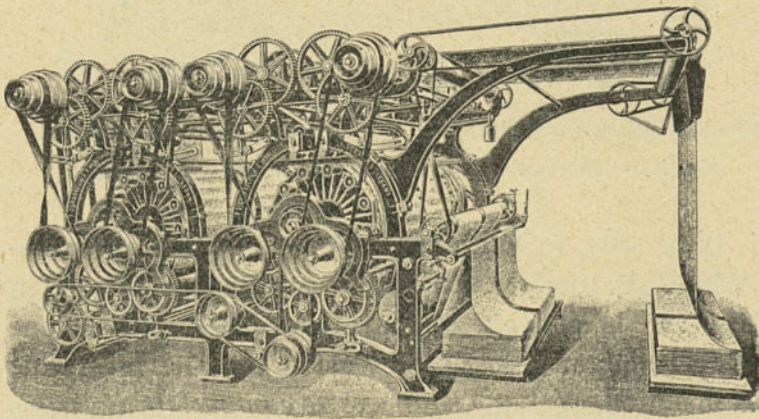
Ensemble d'une machine à lainer (Grosselin).
